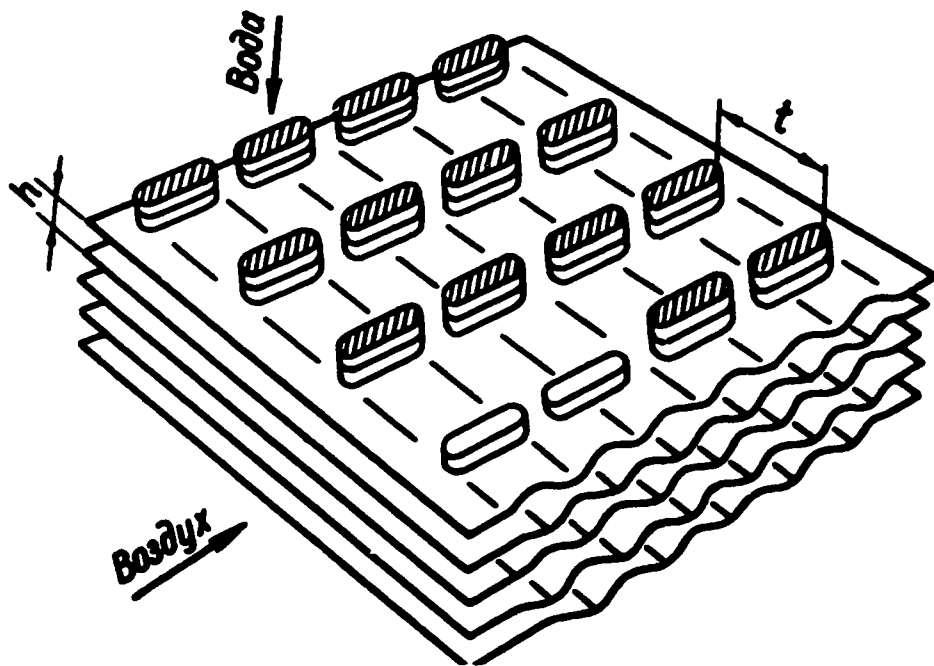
Прямоугольные каналы поверхностей с двухмерными непрерывно сопряженными выступами и канавками в конструкции трубчато-пластинчатого водяного радиатора
